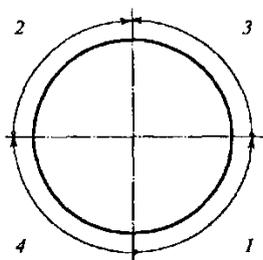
Порядок сварки корневого слоя шва неповоротного стыка
